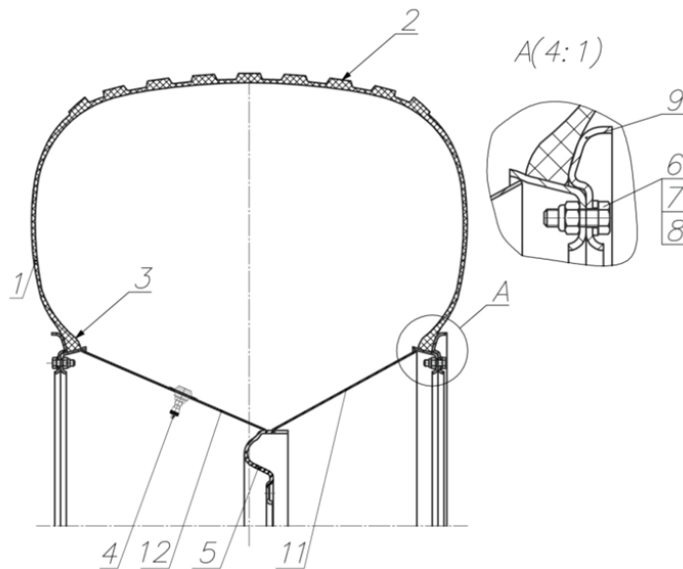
Шина 1300x600-533 ТРЭКОЛ с колесом в сборе: 1 – шина; 2 – протектор шины; 3 – борт шины; 4 – вентиль; 5 – диск колеса; 6 – болт; 7 – шайба; 8 – гайка; 9 – кольцо бортовое обода; 10 – кольцо посадочное обода с фланцем; 11 – конус внутренний; 12 – конус наружный.
